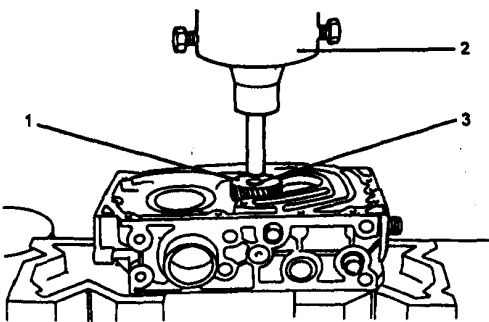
机油泵驱动齿轮与机油泵主动齿轮的装配
